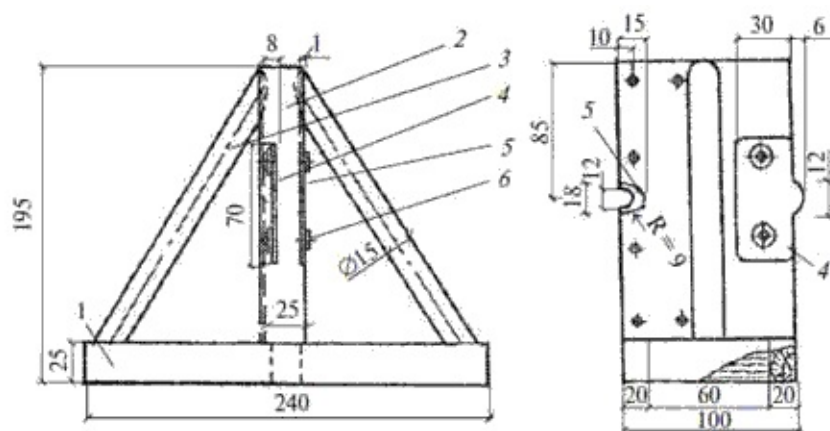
Универсальная рустовка для отделки канавки и валика:
